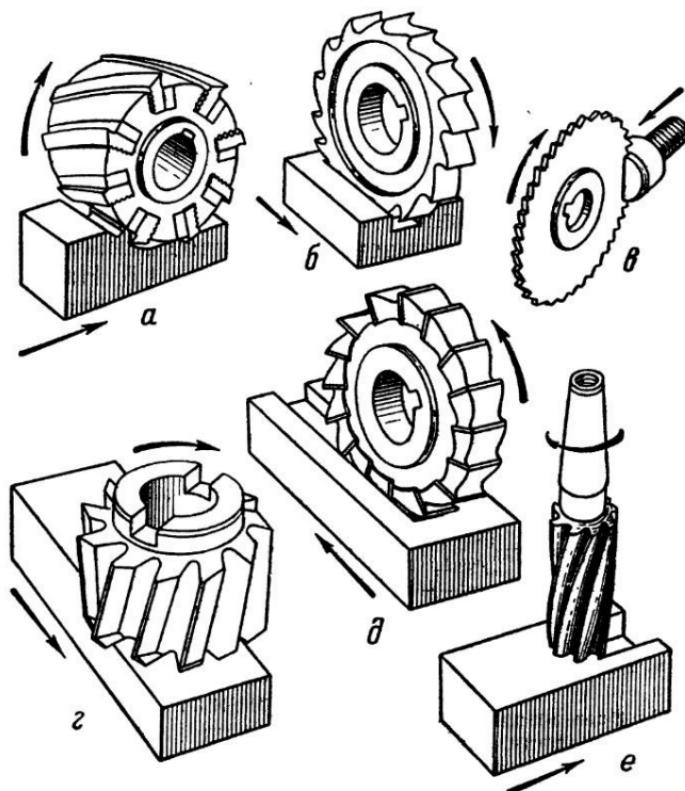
Основные типы фрез: *а* — цилиндрическая; *б* — дисковая пазовая; *в* — шлицевая (прорезная); *г* — торцевая; *д* — дисковая трехсторонняя; *е* — концевая.
